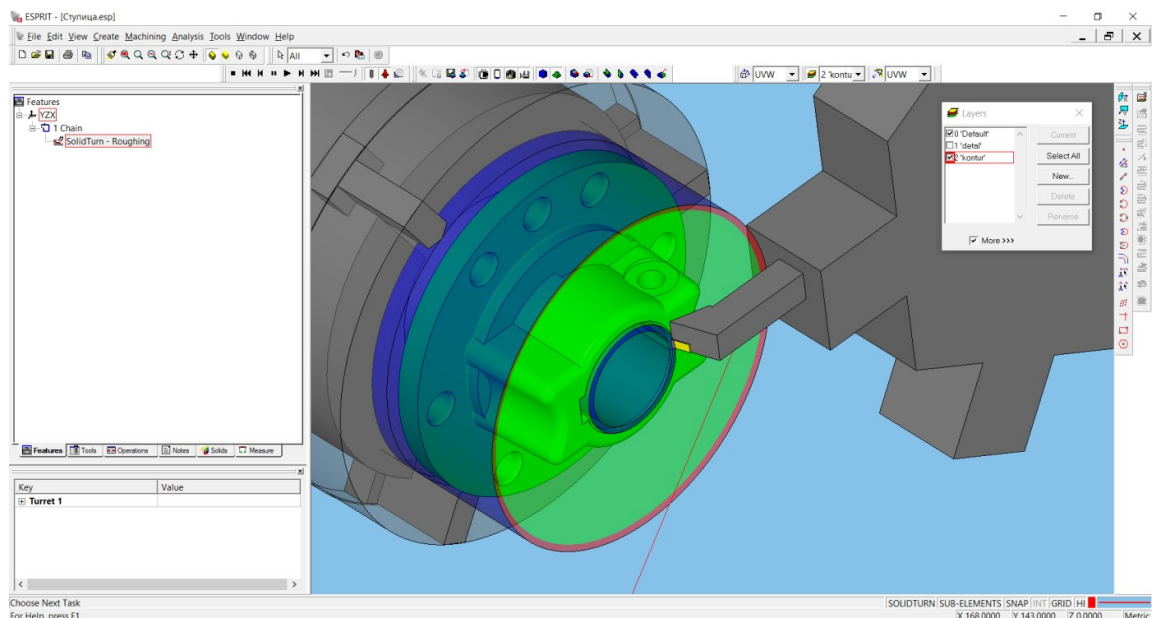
Траєкторія руху інструменту при обробленні фланця
